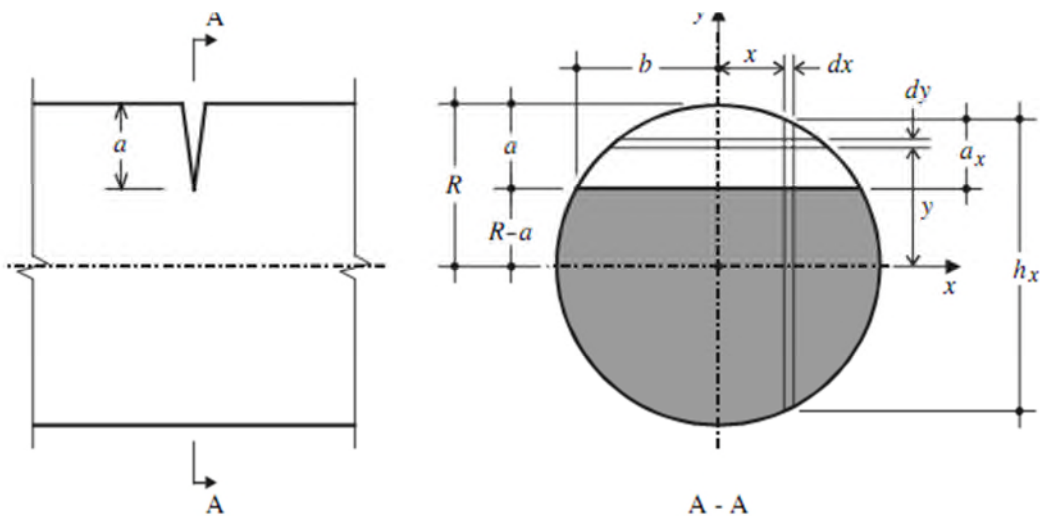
Géométrie d'une section transversale circulaire fissurée.
